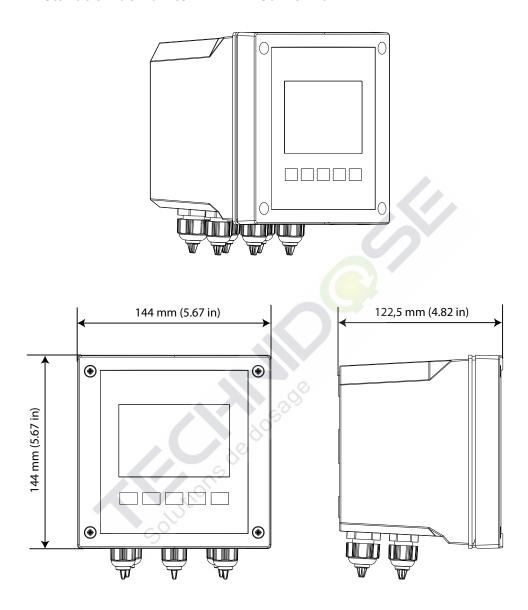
Dimensions et encombrement du dispositif à montage mural
